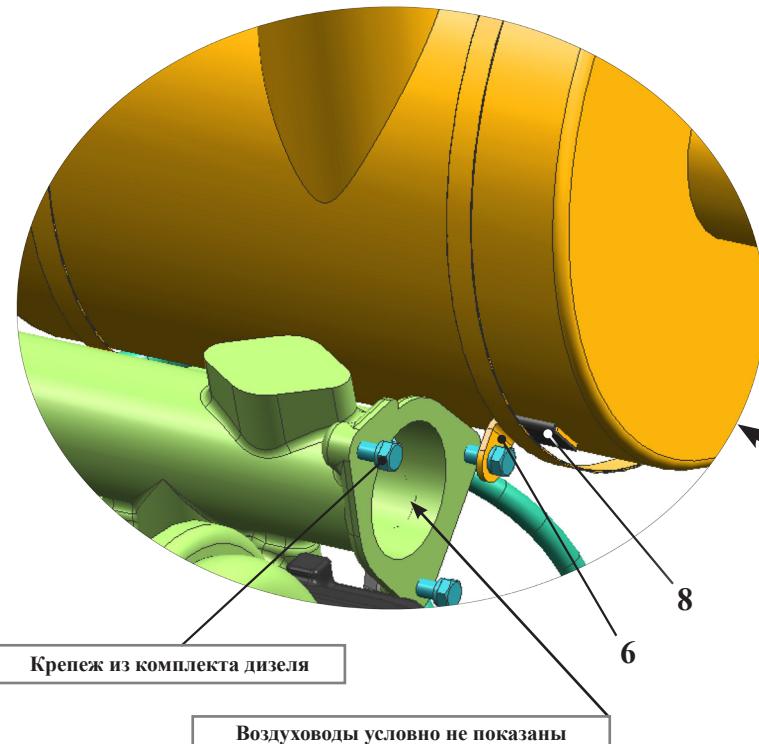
320.11.09.000-Б	Установка воздухоочистителя
